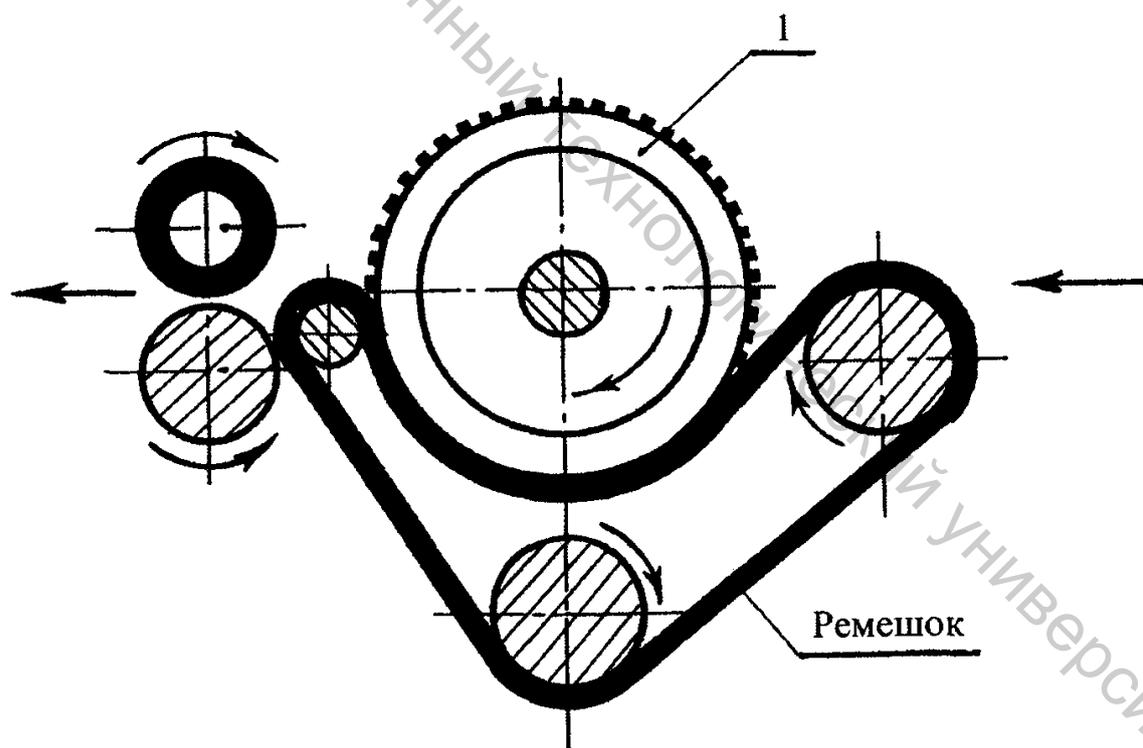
Схема вытяжного прибора конструкции А. Мейера и А. Райляка
